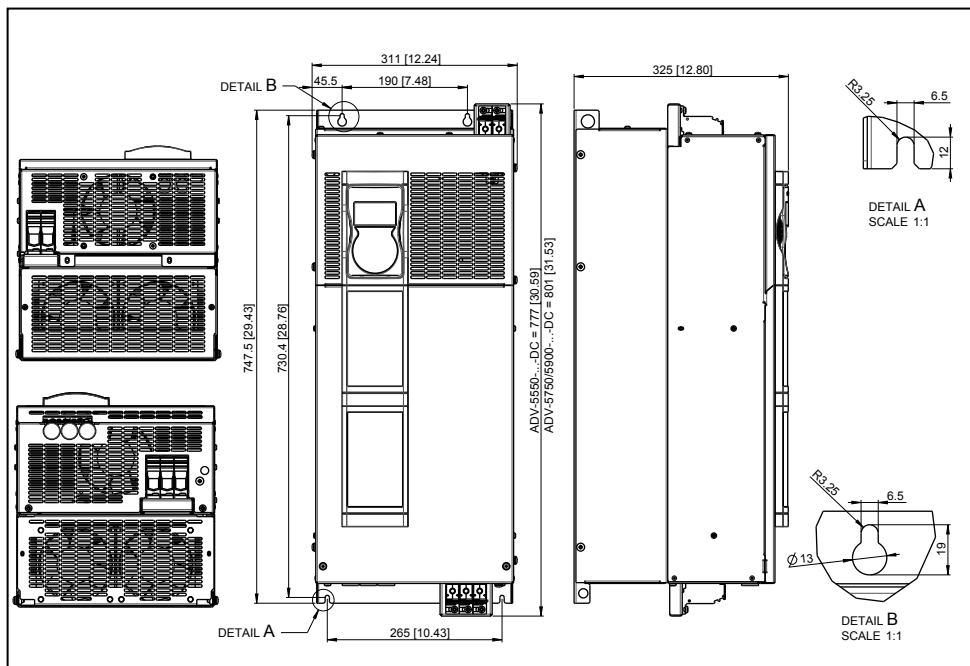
Размеры для типоразмера 5 (ADV200-...-4-DC)
